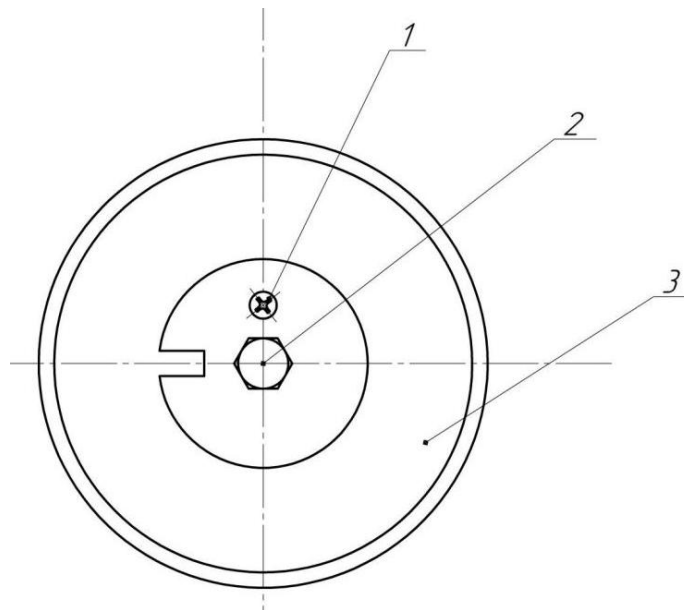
Оправка для контробразца: 1– отверстие под фиксатор, 2– установленный фиксатор
